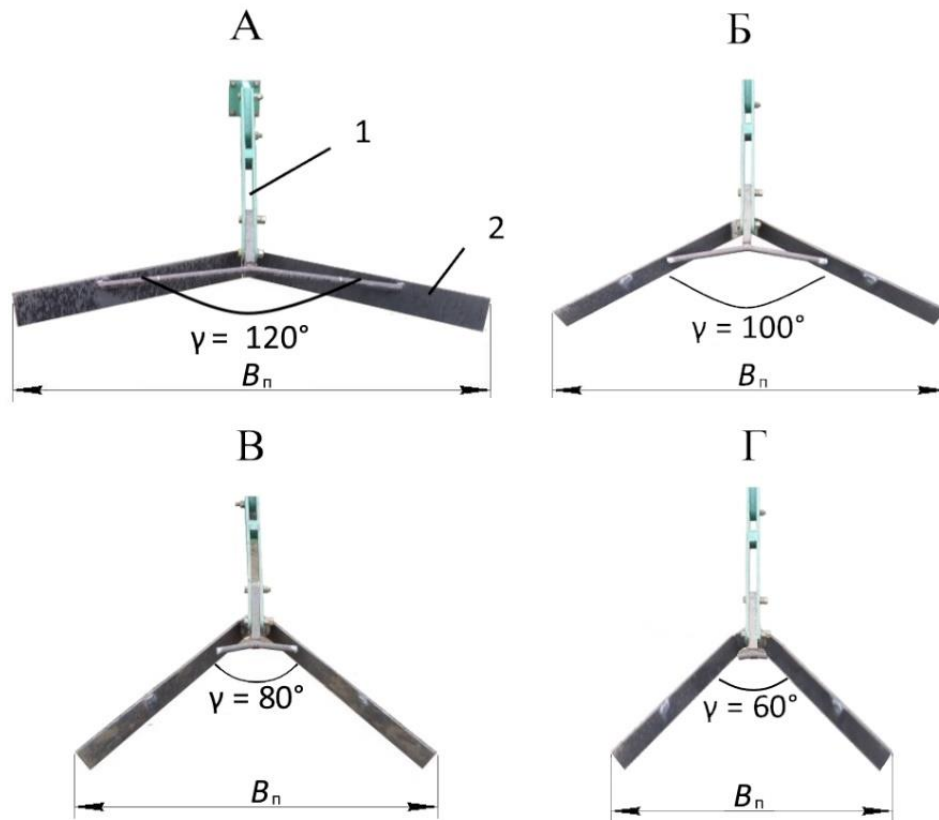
Сталкиватель приспособления №2: 1 – поводок; 2 – пластины;
